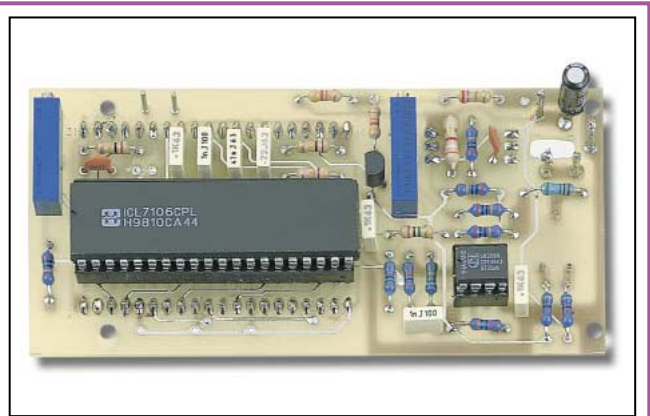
Photo du circuit imprimé vu du côté des composants. De chaque côté du circuit intégré IC2, vous pouvez voir les deux trimmers multitours R9 et R21.
